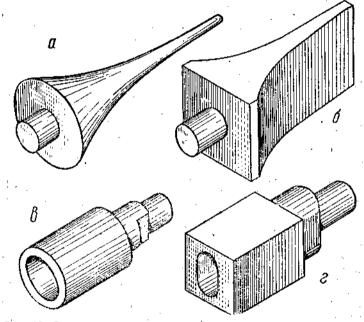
Сменные наконечники для сварки пластмасс ультразвуком: a — точечной сварки, δ — ножевой для шевно-шаговой сварки, θ — для контурной сварки кольцевых инов, ϵ — для контурной сварки швов прямо-угольного сечения.
